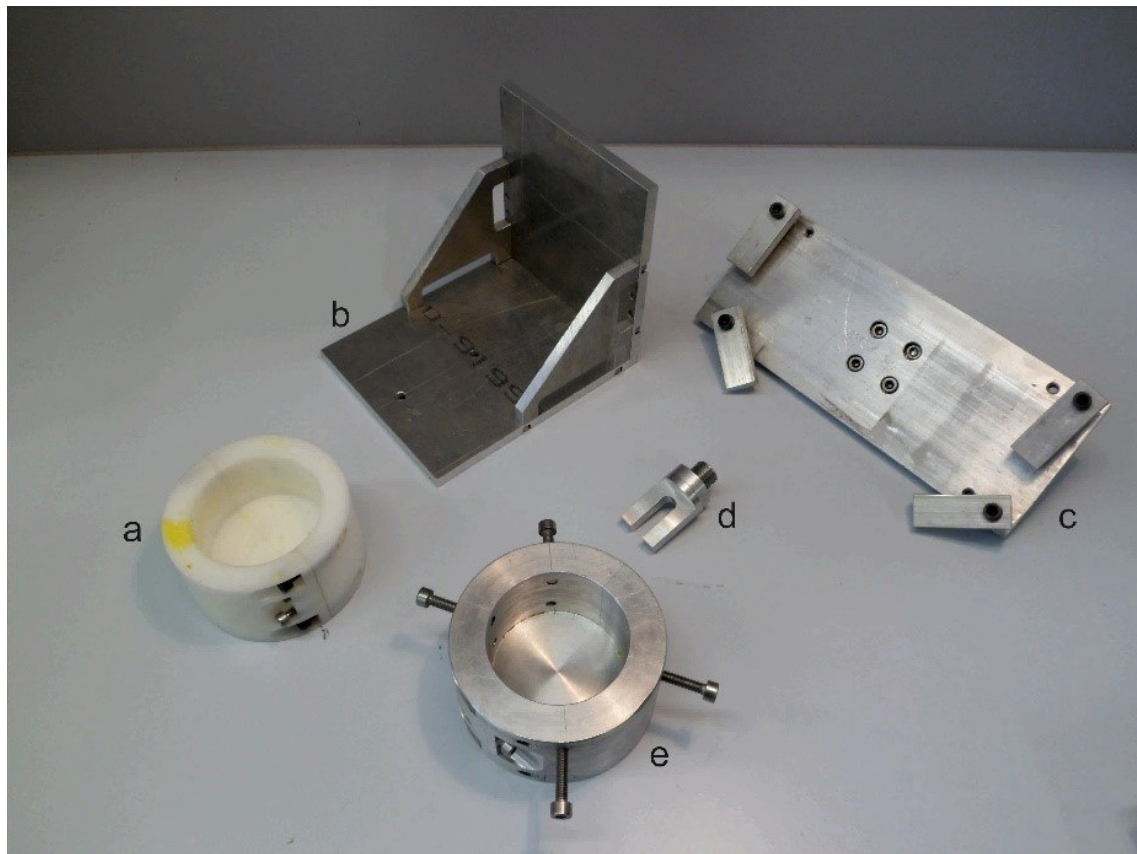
Gussform und Bauteile der Belastungsvorrichtung: (a) Gussform, (b) Versuchsplattform, (c) Befestigungsplatte, (d) Kraftgeber, (e) Aufnahmebehälter
